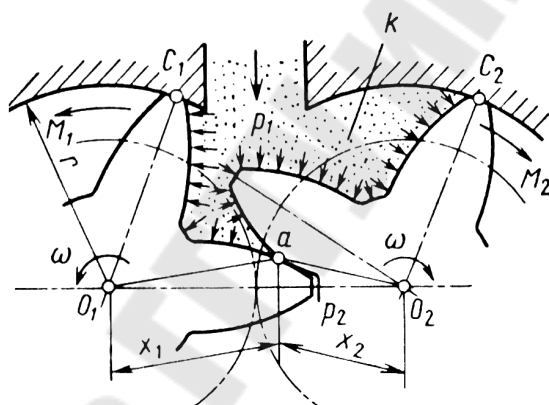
Схема рабочей камеры шестеренного гидромотора
